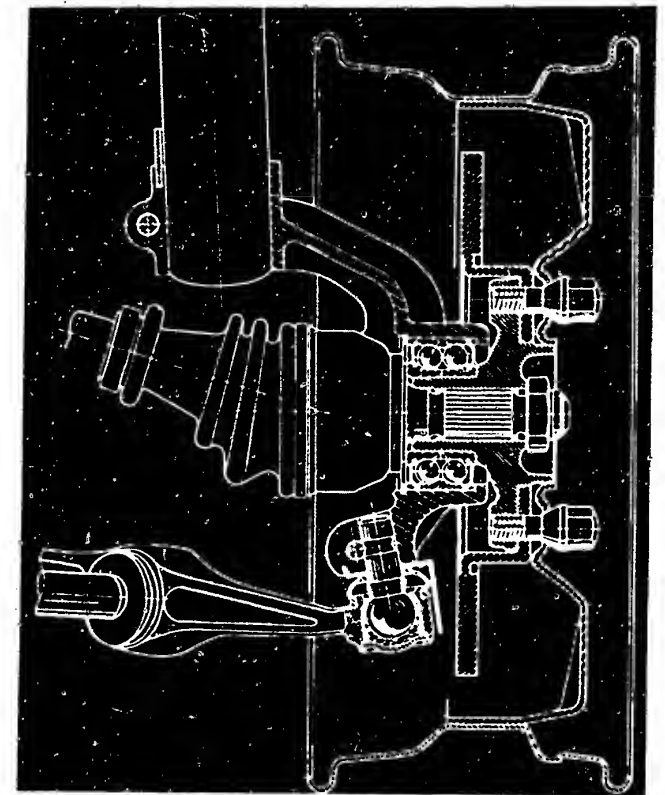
Schnitt durch die Vorderradlagerung mit dem voreingestellten Lager.
